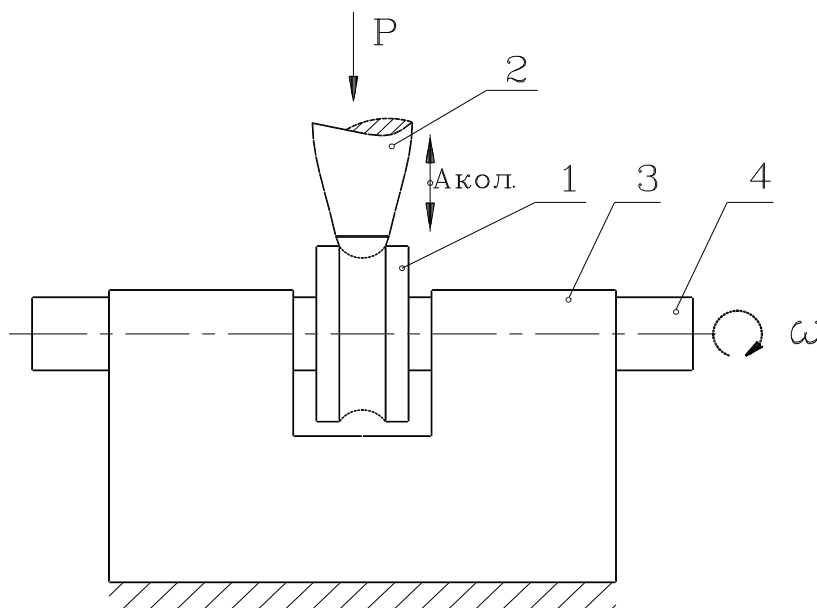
Схема безабразивного суперфиниширования: 1. Опытный образец- внутреннее кольцо шарикового подшипника. 2. Инструмент-волновод с твердосплавным сферическим наконечником. 3. Призма. 4. Цилиндрическая оправка
